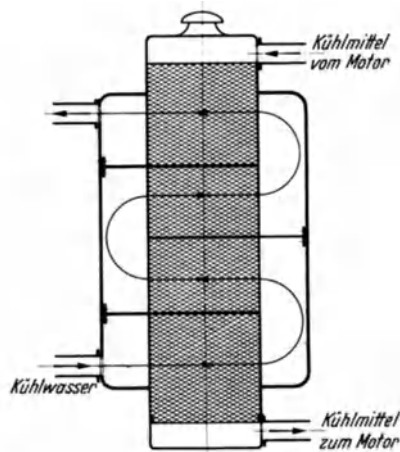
Mit Wasser rückgekühlter Sonderkühler.
